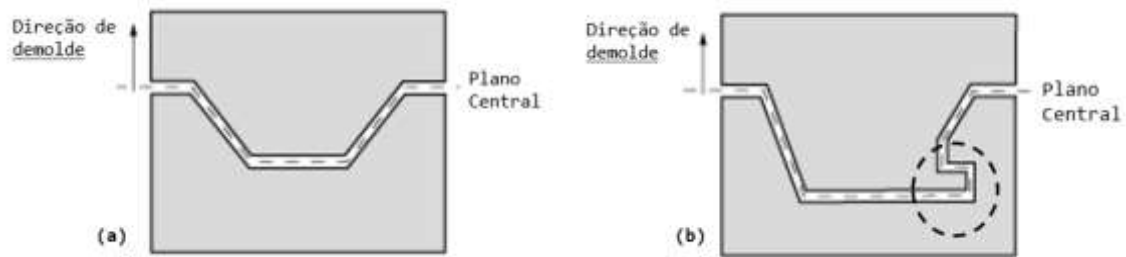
Problema de demoldagem. a) Geometria possível de demolde. b) Geometria impossível de demolde, especialmente na região destacada.
